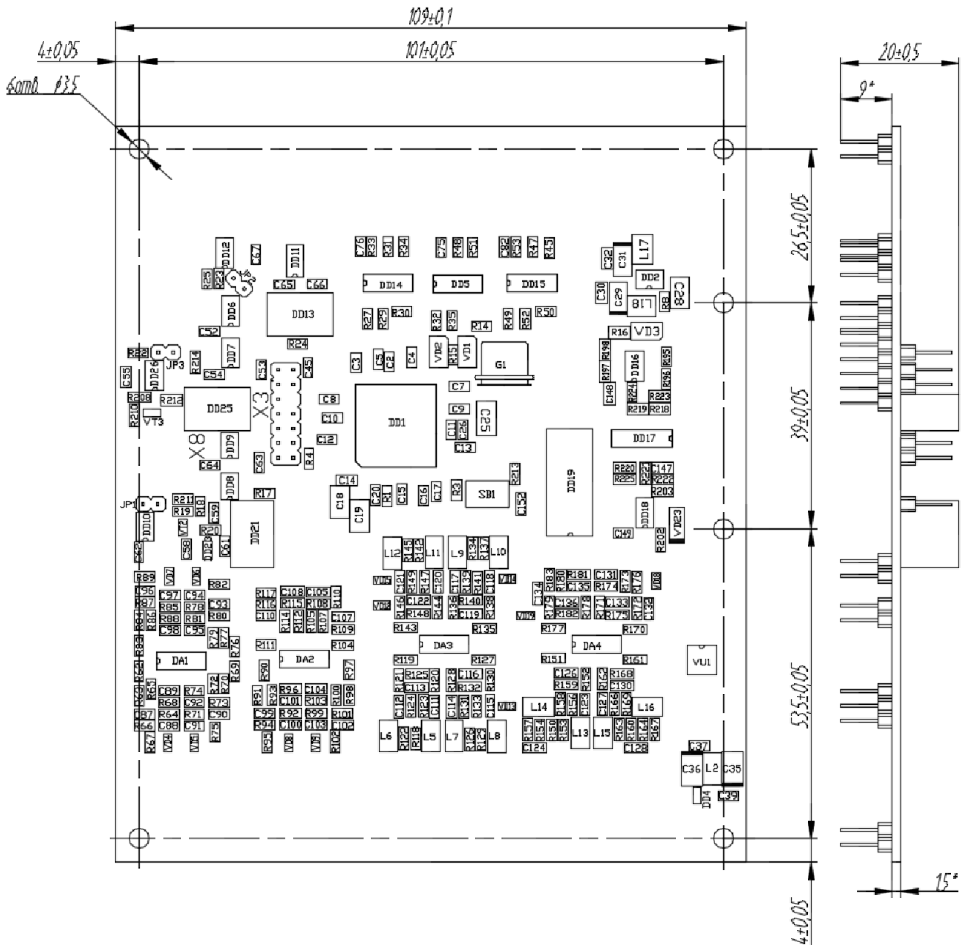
Габаритные и присоединительные размеры платы контроллера МК17.3 исполнение 4
